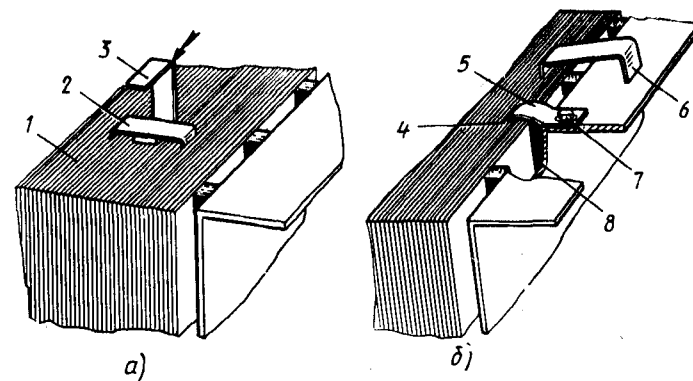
Снятие скоб перед прессовкой (а) и установка заземляющей шинки (б):
